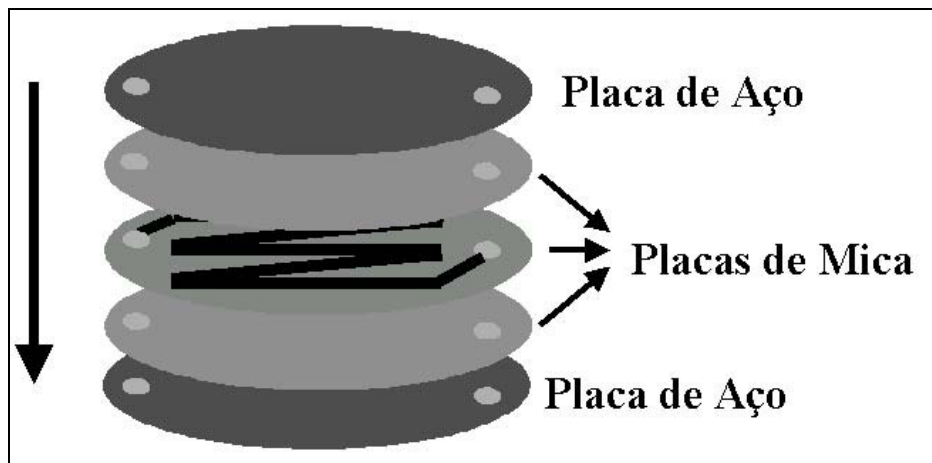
Esquema de montagem das placas do aquecedor.
